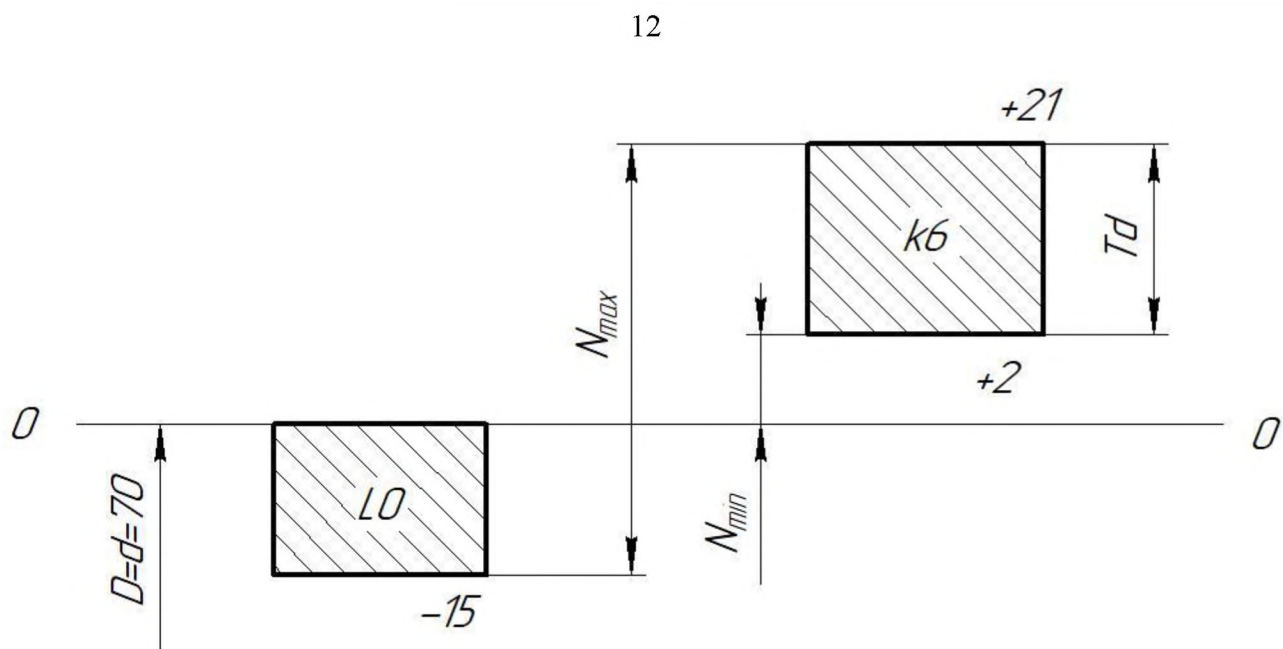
Схема полів допусків з'єднання підшипник - вал
